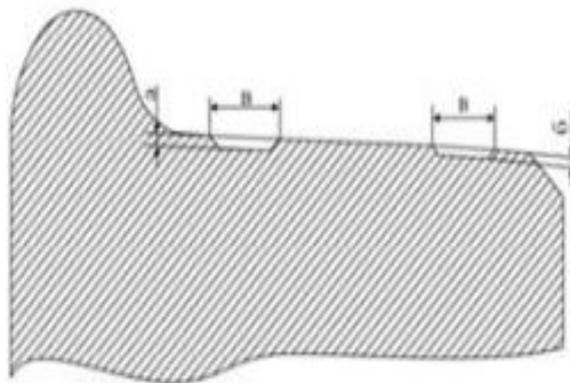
Тормозное кольцо позволяет разработать процесс измерения поверхности качения конструкции качения колеса
